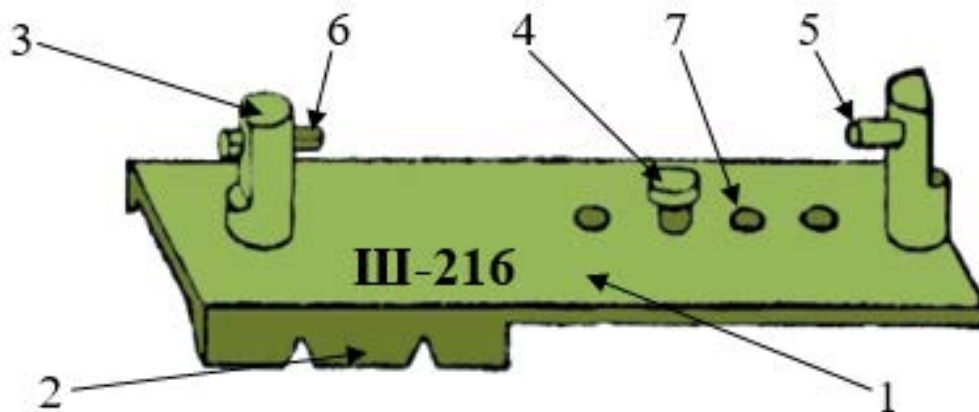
Металева шпора Ш-216 (1 – плита; 2 – гребні плити; 3 – стійка; 4 – обмежувач; 5 – фіксатор; 6 – шплінт; 7 – отвір для обмежувача).
